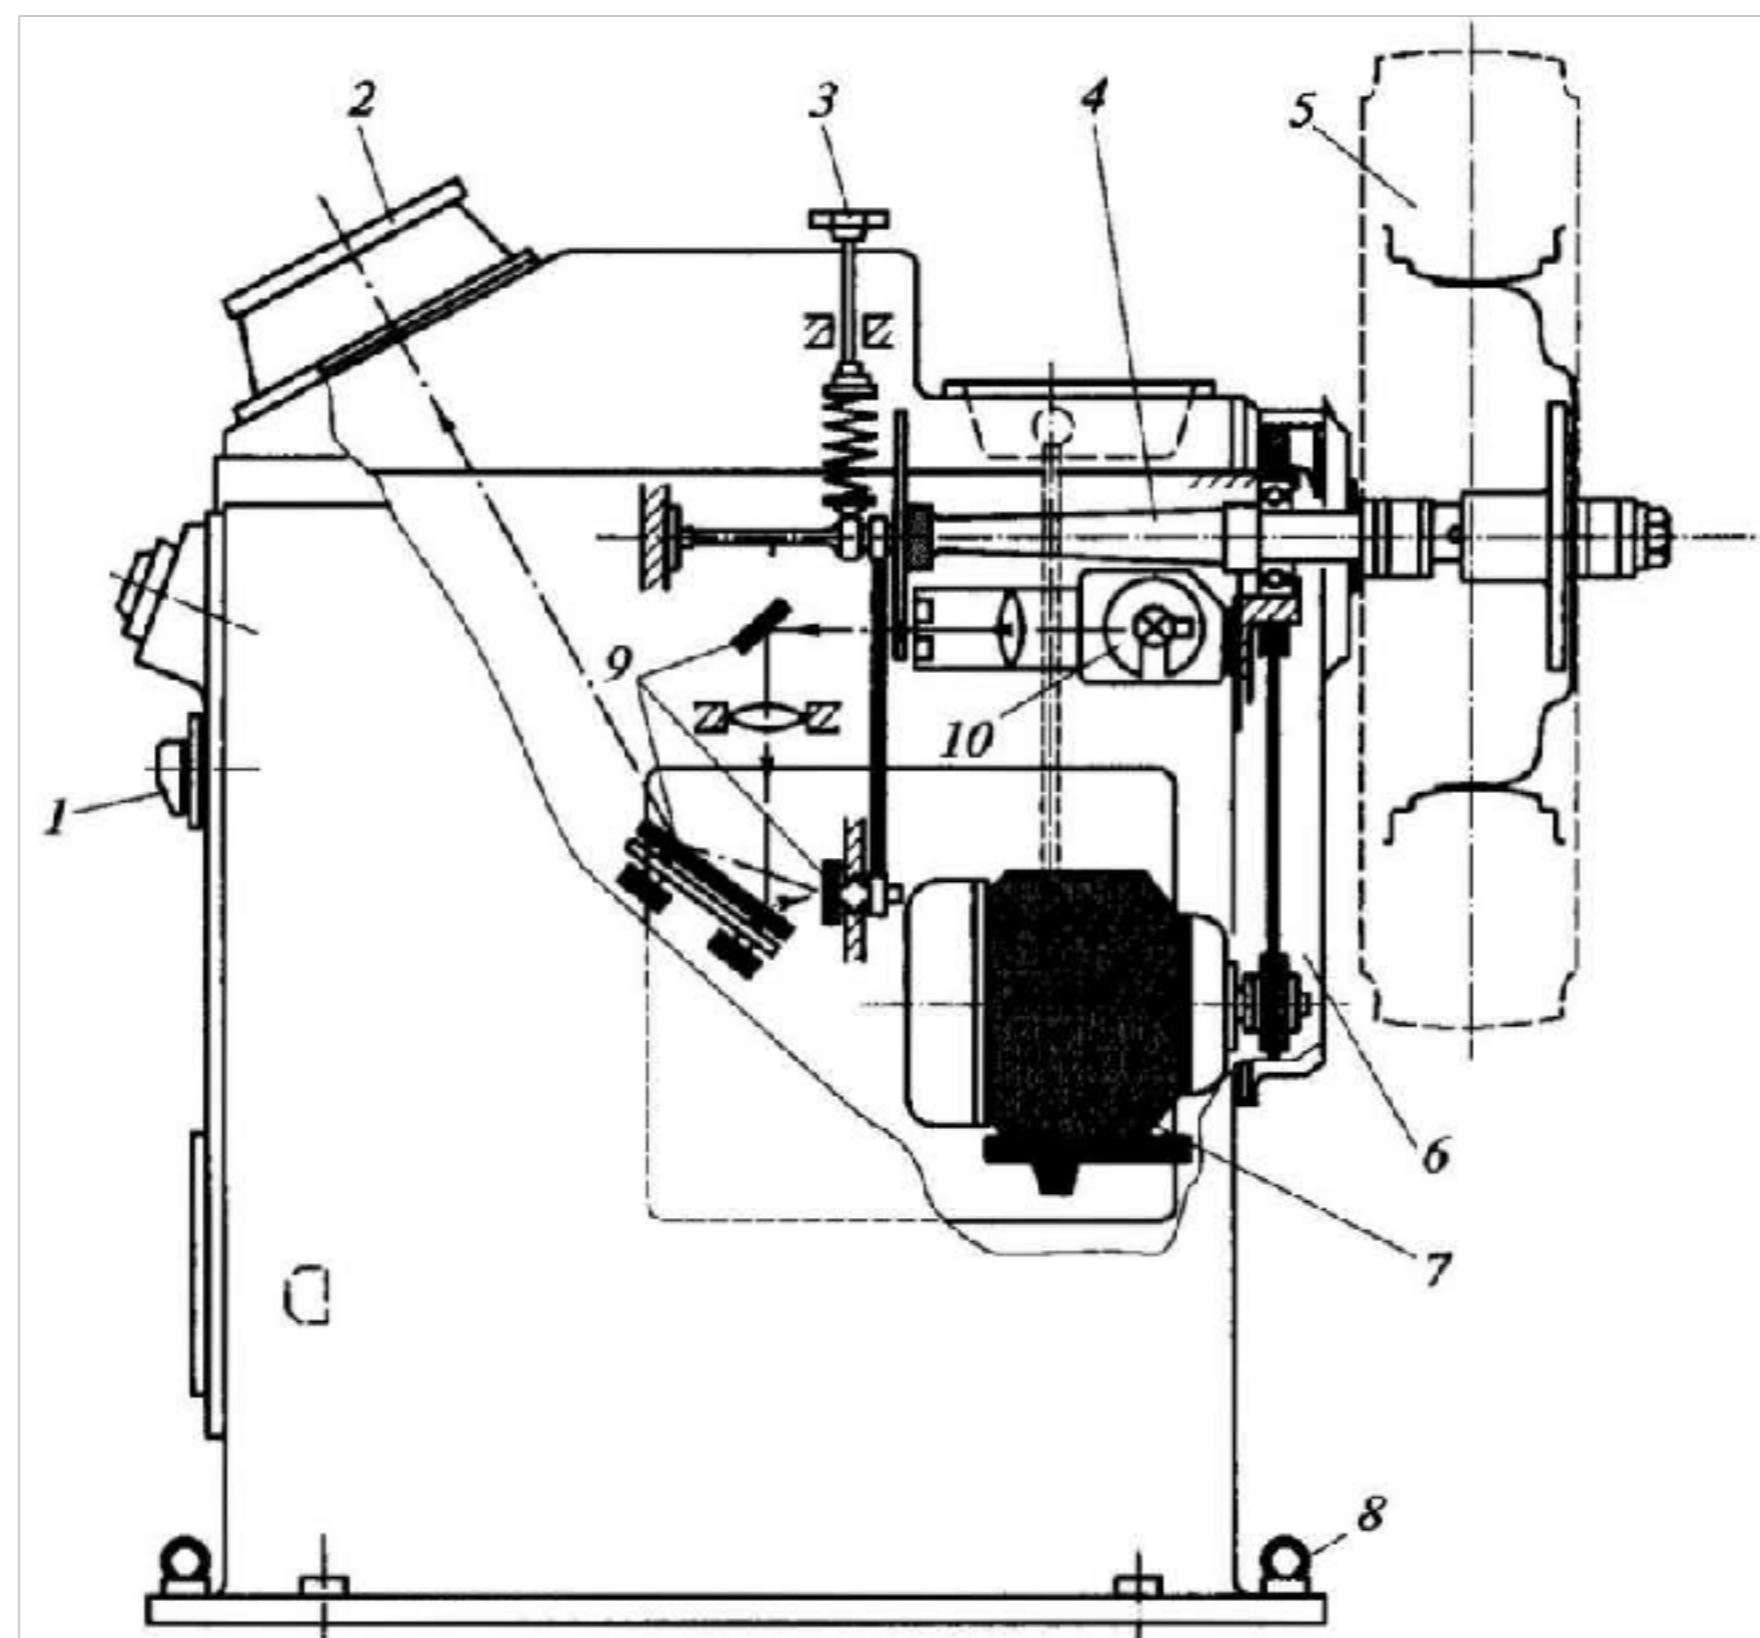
Стенд для балансировки колес, снятых с автомобиля: 1 — выключатель станка; 2 — экран станка; 3 — регулировочный винт; 4 — балансировочный вал; 5 — колесо, снятое с автомобиля; 6 — ремни привода станка; 7 — электромотор привода; 8 — транспортные рым-болты; 9 — зеркала, направляющие отклоненный луч на экран; 10 — источник света
